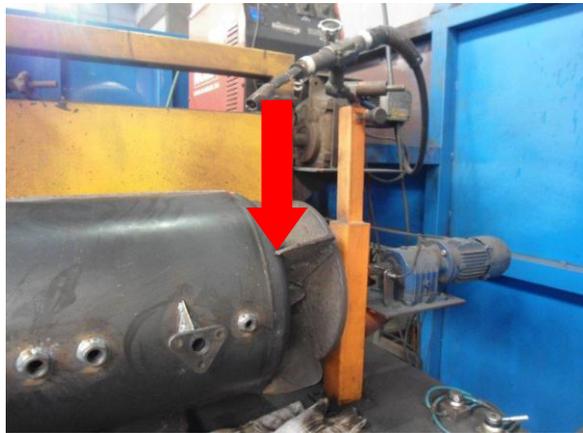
Dispositivo de Solda Ajustado. Fonte: O autor.
